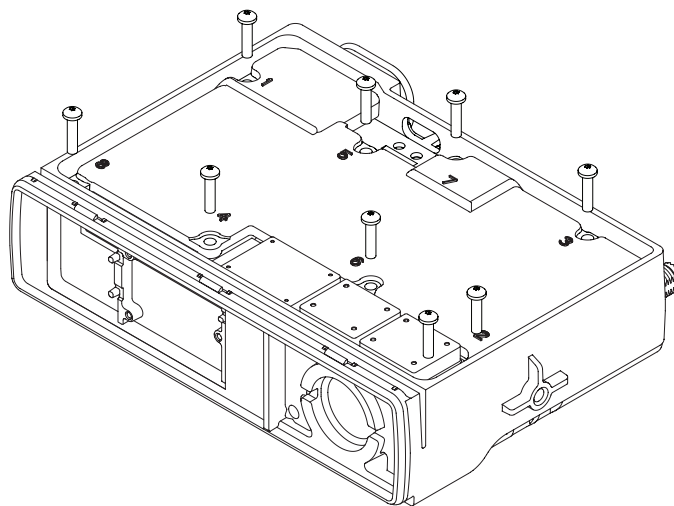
Montagem da Proteção Principal Fundida no Chassi
